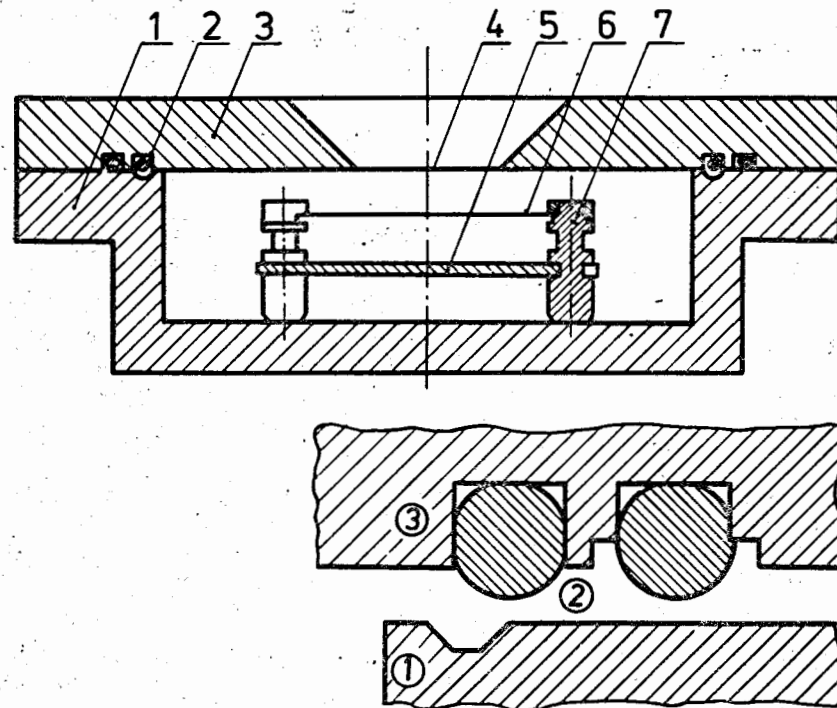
Поперечный разрез многонитевой пропорциональной камеры для альфа-спектрографа. 1 - корпус, 2 - уплотнение, 3 - крышка, 4 - верхний катод /лавсановая пленка с напыленным алюминием/, 5 - нижний катод /стальная пластина/, 6 - анодная нить, 7 - изолятор /тефлоновый столбик/.
